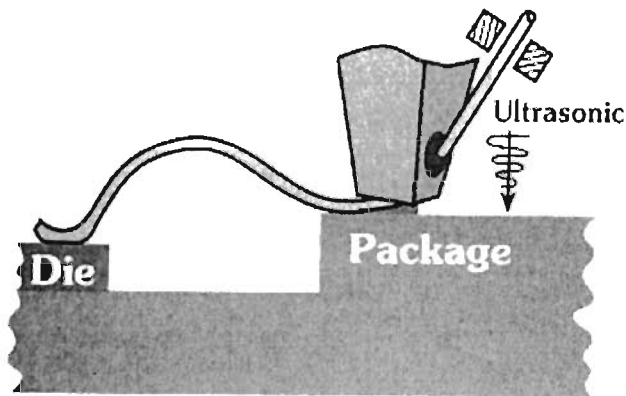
Soldado por medio de herramienta de cuña (hecho con herramienta K&S Micro-Swiss).
